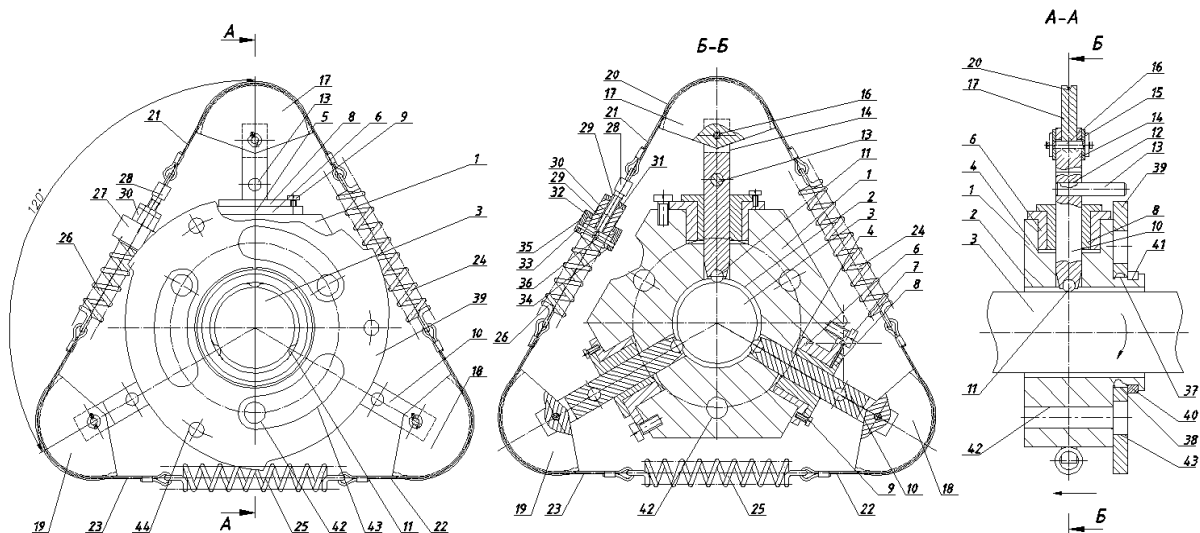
Інструмент для чистового фінішного оброблення зовнішніх циліндричних поверхонь поверхневим пластичним деформуванням
